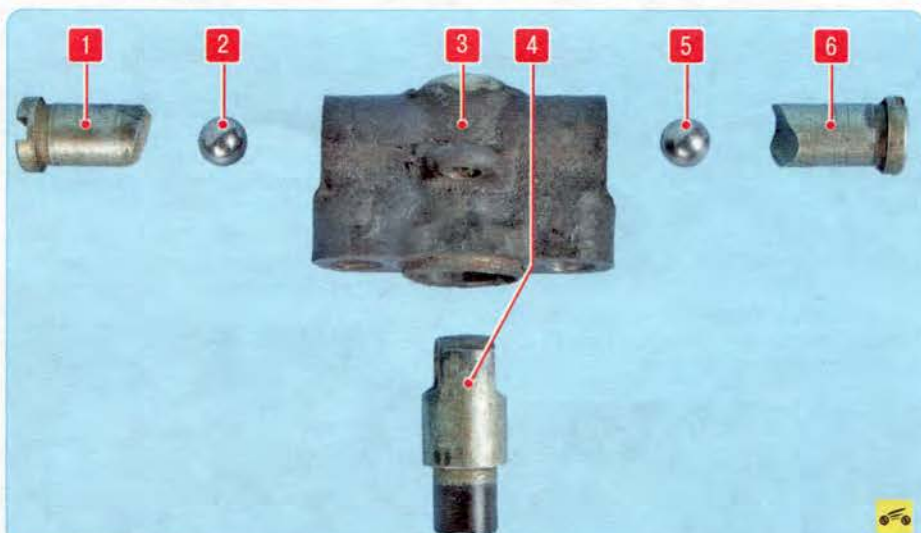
Детали разжимного механизма стояночного тормоза: 1, 6 – толкатели разжимного механизма; 2, 5 – шарики; 3 – корпус разжимного механизма; 4 – корпус шариков разжимного механизма
